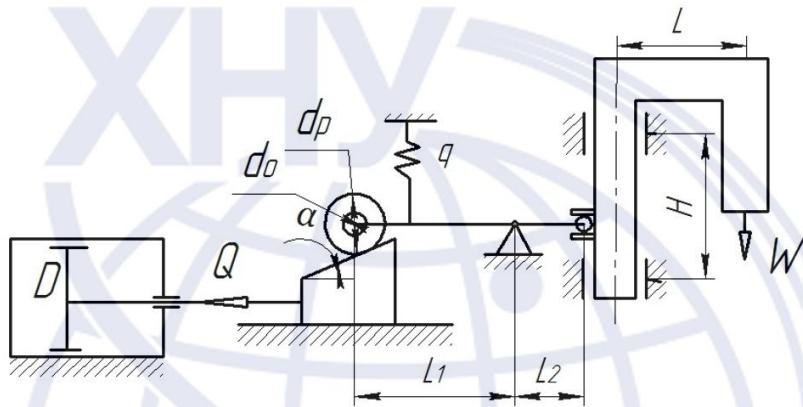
Кінематична схема механізму затиску пристрою
